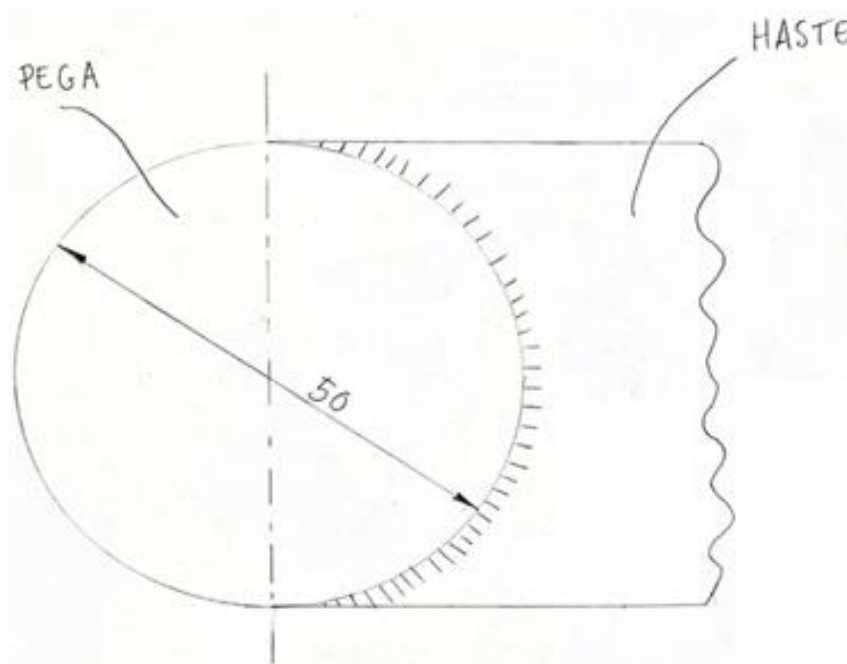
Esboço da Soldadura entre a Pega para o Operador e o Perfil tubular da haste.
